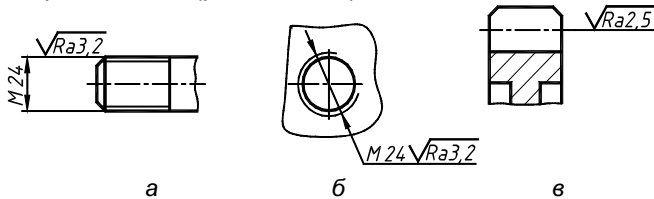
Примеры указания шероховатости: а - на наружной резьбе; б - на внутренней резьбе; в - на рабочей поверхности зубьев зубчатых колесах
